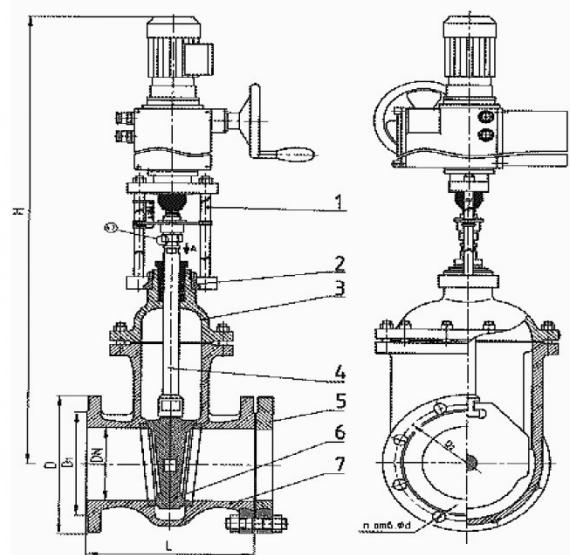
Элементы задвижки (общий вид): 1 – шпилька; 2 – резьбовая втулка; 3 – крышка; 4 – шпиндель; 5 – фланец трубы; 6 – клин; 7 – корпус
